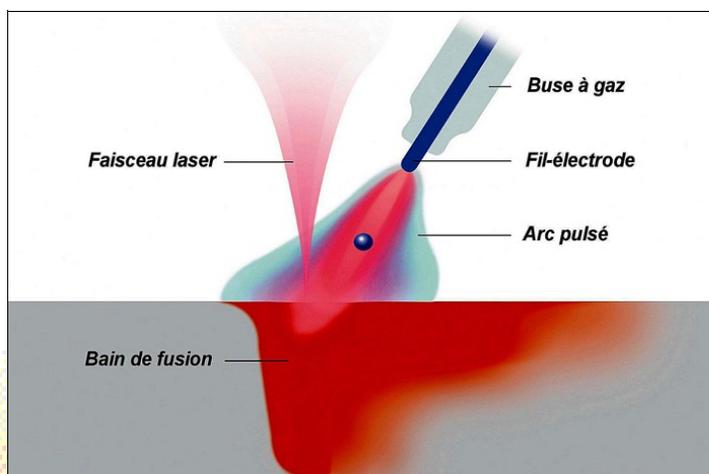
schéma de principe du procédé de soudage hybride arc-laser (HLW)
